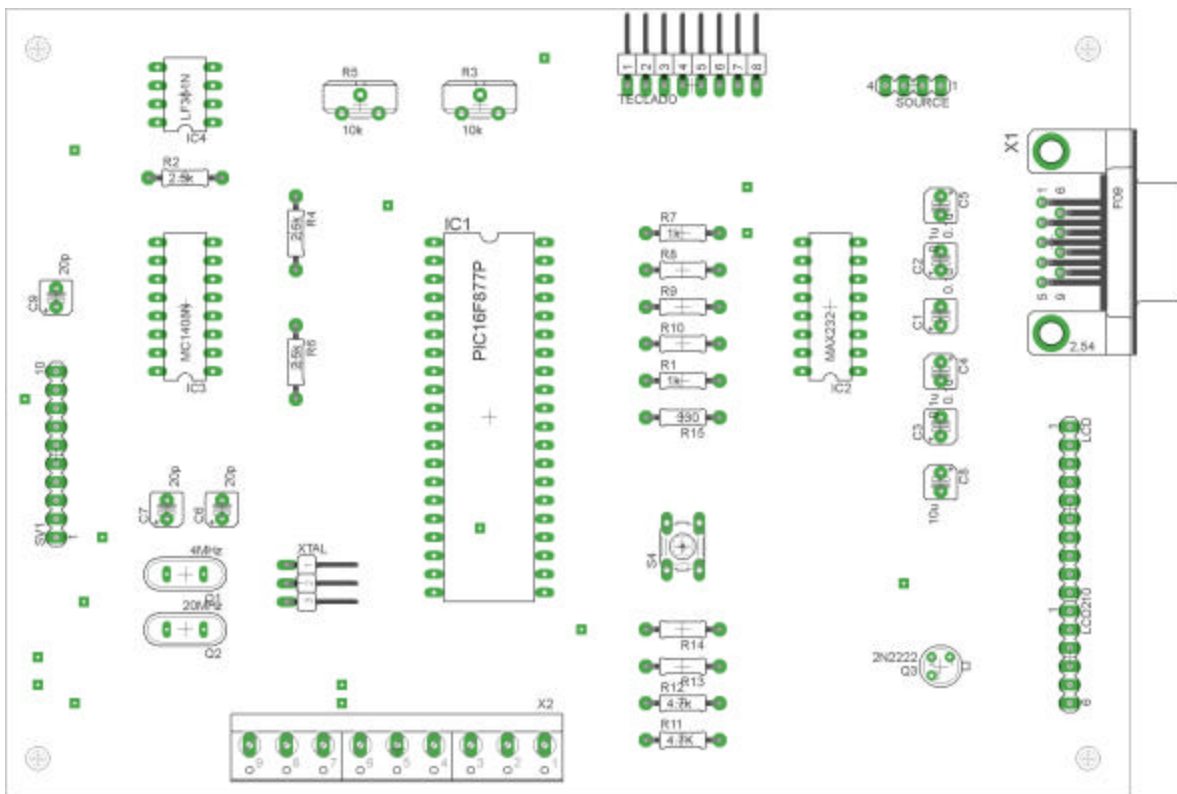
Ubicación de componentes en PCB de tarjeta de control.
